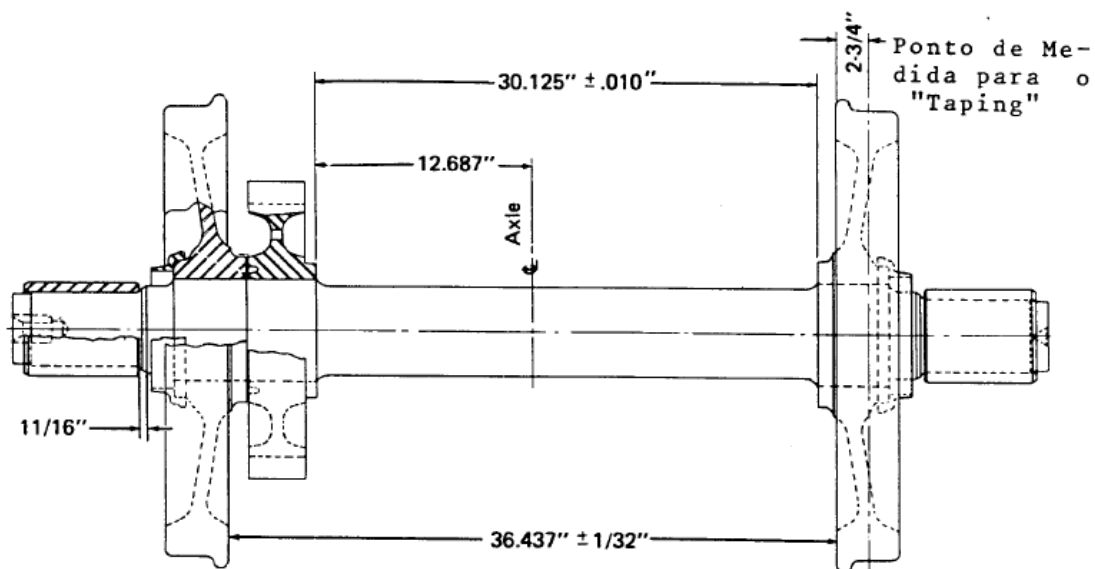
Dimensões para montagem do conjunto de rodas DDM45
